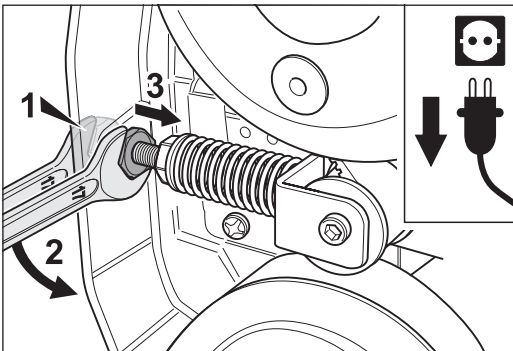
Die Schraube des Zahnriemenspanners mit einem Gabelschlüssel festhalten (1) und gleichzeitig mit einem zweiten Gabelschlüssel die Kontermutter bis an die Spannmutter schrauben (2 + 3).
